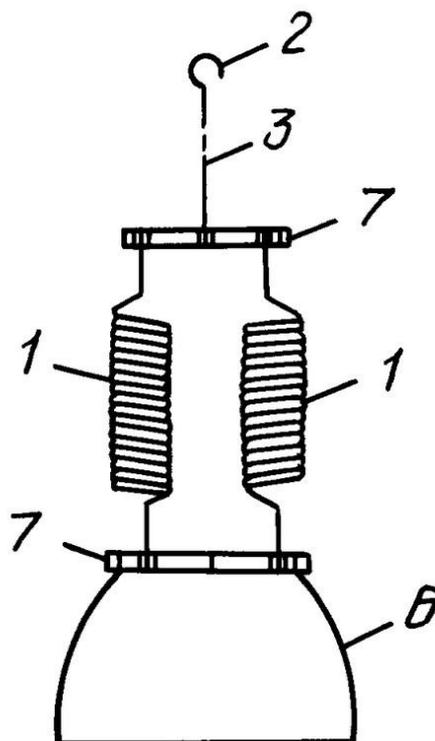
Устройство с двумя силовыми элементами из пружины
